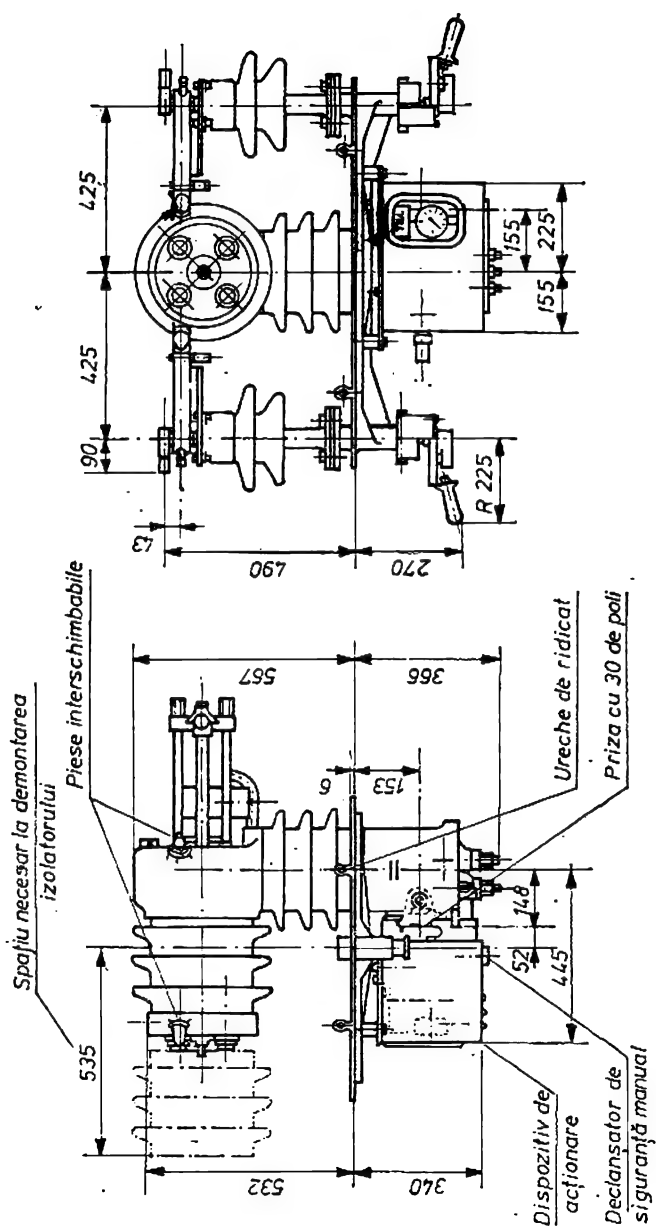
Înteruptor cu aer comprimat tip IAC-25 pentru LE-5100 kW. Dimensiuni gabarit.
